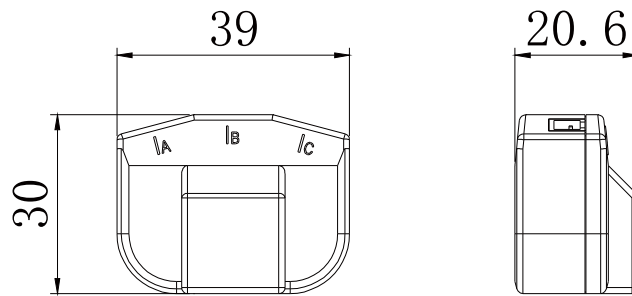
Внешний вид и габаритные размеры модуля коммутации Z1
